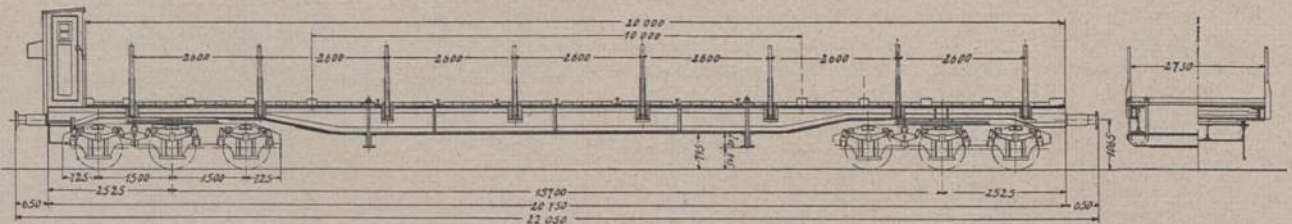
Sechssachsiger Plattformwagen für 52,5 t Ladegewicht mit Bremse
